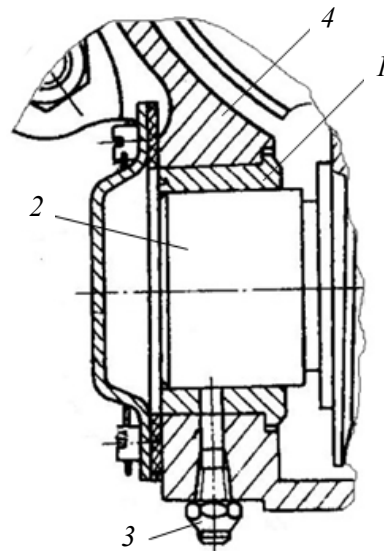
Фрагмент узла подъемного механизма артиллерийского орудия: 1 – втулка; 2 – вал (шип червячного валика); 3 – масленка; 4 – корпус механизма
